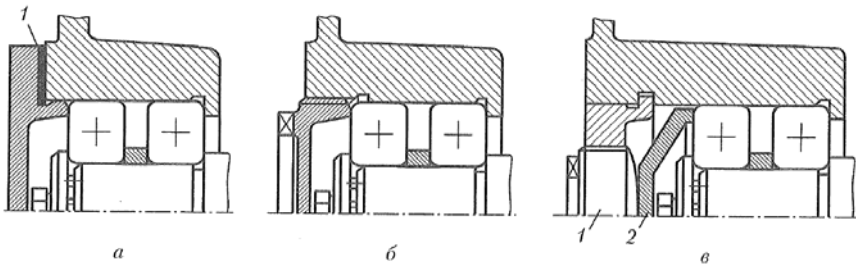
Способы регулирования зазоров в подшипниках перемещением наружного кольца: а – набором тонких металлических прокладок 1; б – винтом; в – винтом 1 с установочной шайбой 2
